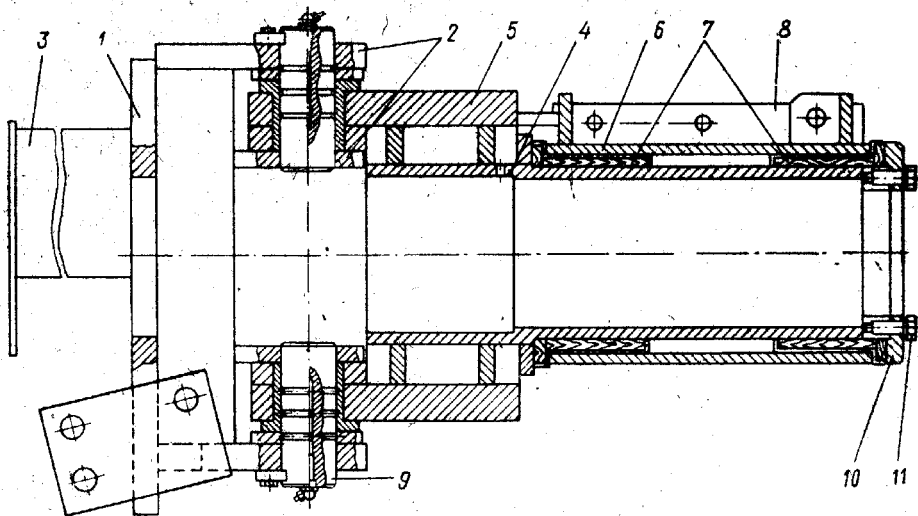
Центральный универсальный шарнир активного полуприцепа в сборе:
